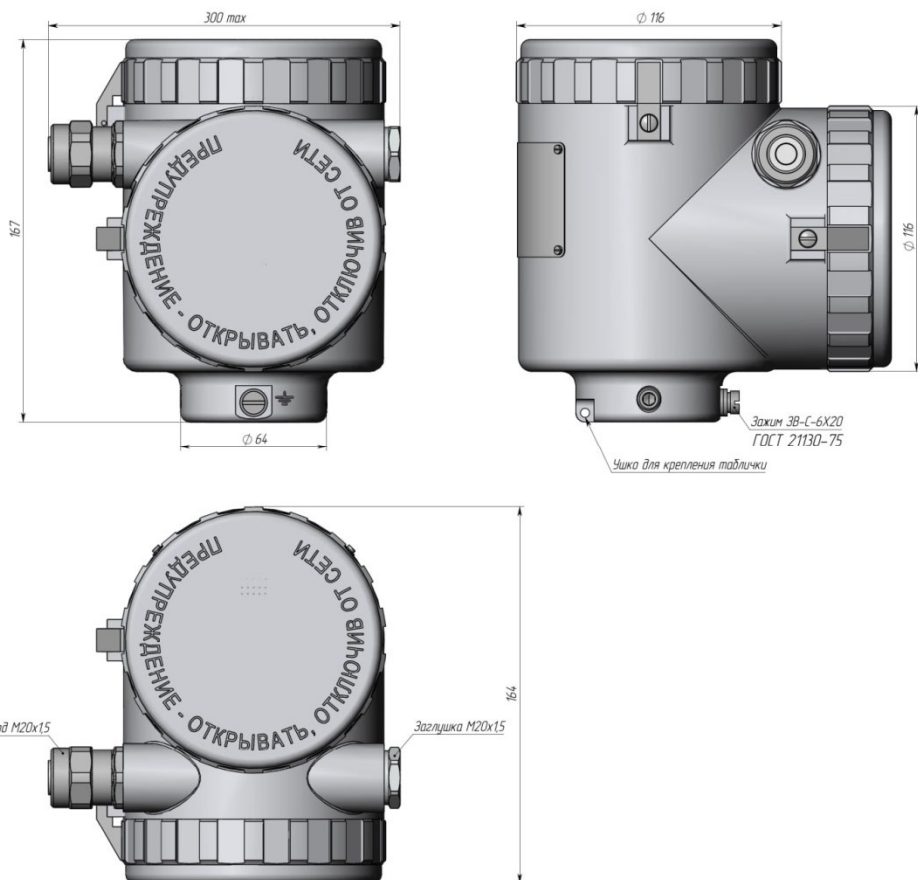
Габаритные и установочные размеры алюминиевого корпуса блока электронного преобразователя. IP68.
